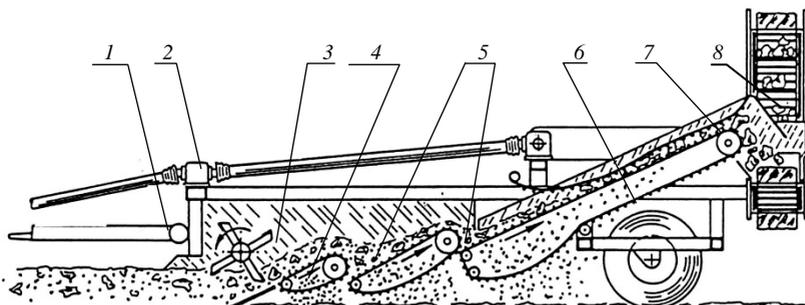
Схема работы машины для очистки почвы от камней: 1 – дышло прицепное; 2 – вал карданный; 3 – ротор измельчительный; 4 – лемех; 5 – транспортеры сепарирующие; 6 – транспортер выгружающий; 7 – ворошилка; 8 – устройство направляющее
